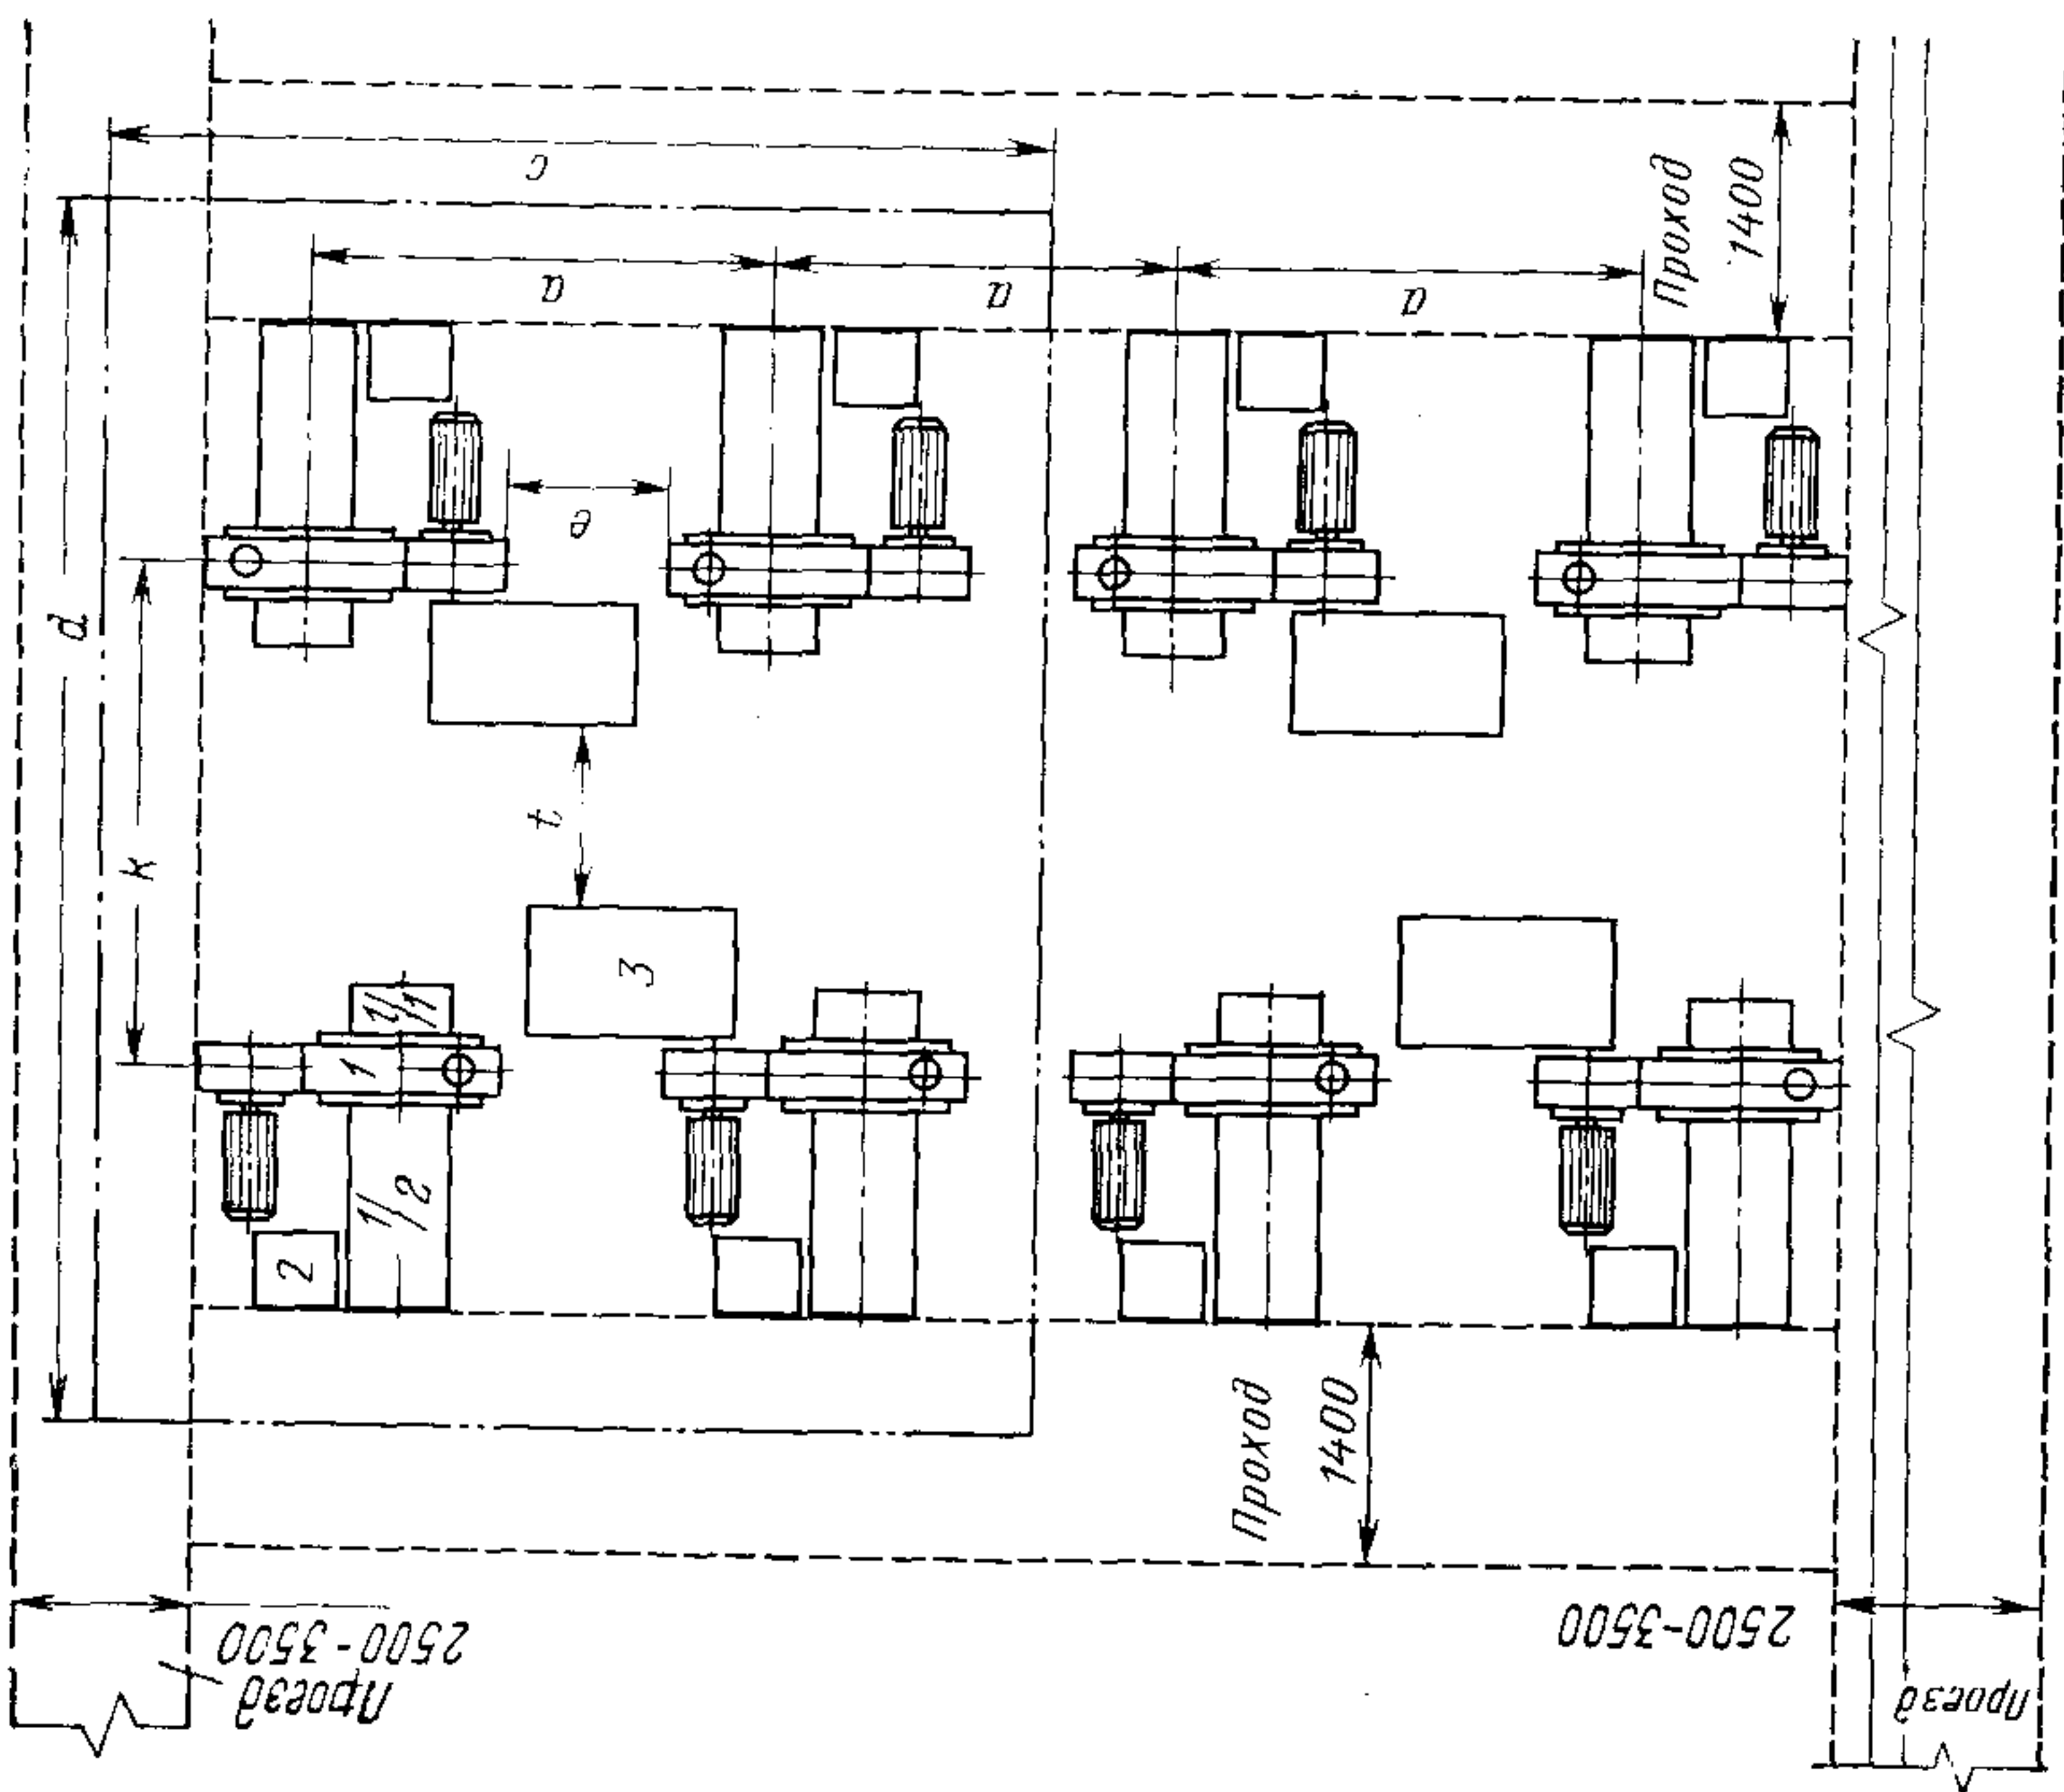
Расположение прессов-автоматов со шнековой приставкой на рабочем месте (вариант второй): 1 — пресс-автомат; 1/1 — устройство для выгрузки изделий; 1/2 — шнековая приставка; 2 — винтовая загрузчик; 3 — рабочий стол (один на два прессы).
